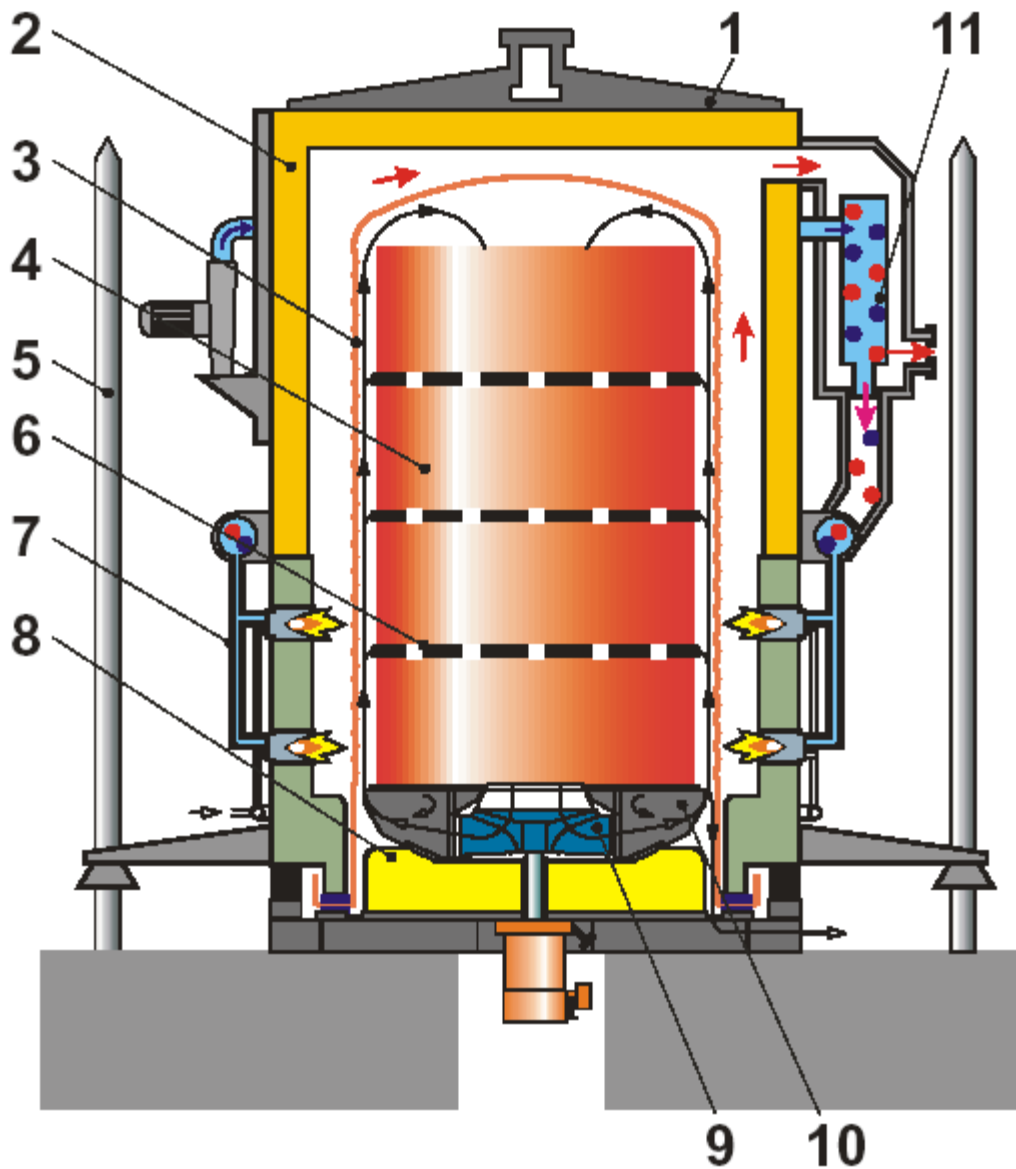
Нагрівальний ковпак: 1 – корпус печі; 2 – футеровка; 3 – муфель; 4 – садка; 5 – напрямна стійка; 6 – конвекторне кільце; 7 – трубна розводка печі; 8 – стенд відпалу; 9 – стендовий вентилятор; 10 – направляючий апарат; 11 – рекуператор
